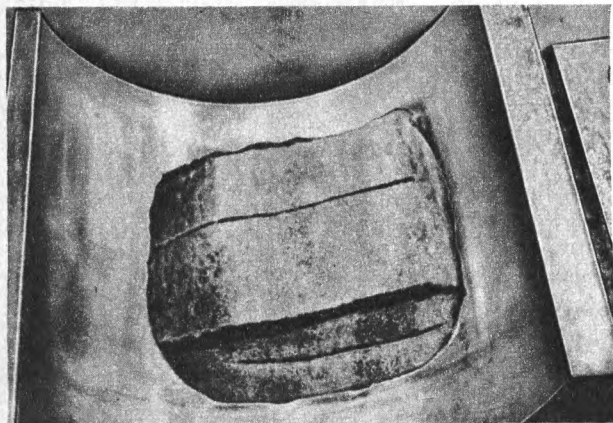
Крышка моторно-осевого подшипника с войлоком, продавленным внутрь масляной ванны. На войлоке видны следы торца окна вкладыша подшипника
